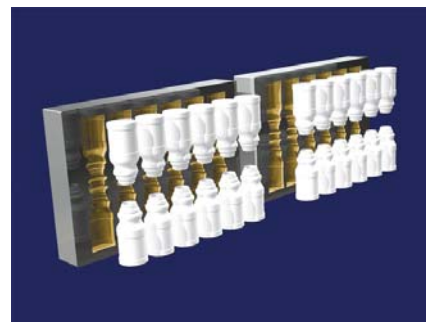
O sistema de corte do material soprado, apresentado pela Bekum, permite a moldagem de dois frascos por cavidade do molde
